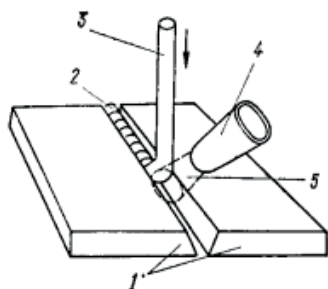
Схема сварки пластмасс нагретым газом с применением присадочного материала: 1 – свариваемые изделия, 2 – сварочный шов, 3 – присадочный материал, 4 – наконечник нагревателя, 5 – струя нагретого газа
